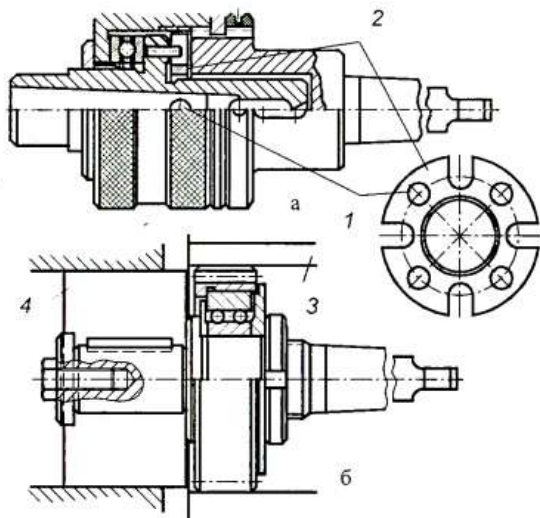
Допоміжний інструмент для закріплення розвірток:
